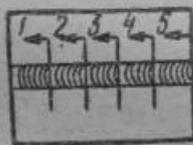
Сварка швов средней длины, обратнo-ступенчатым способом (1—5 — последовательность наложения швов)
